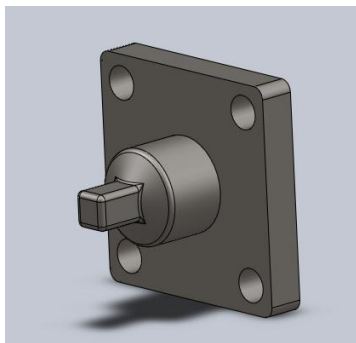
Vista del ensamble de un adaptador y la placa que lo sujeta al bastidor
